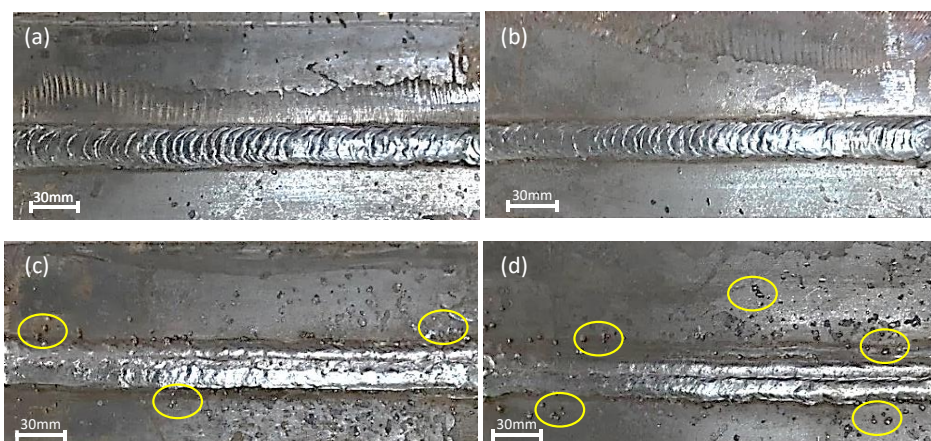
Aspecto Visual Cordões Soldados. a) Com tecimento (C1), b) Com tecimento (C2), c) Filetado (F1), d) Filetado (F2).
